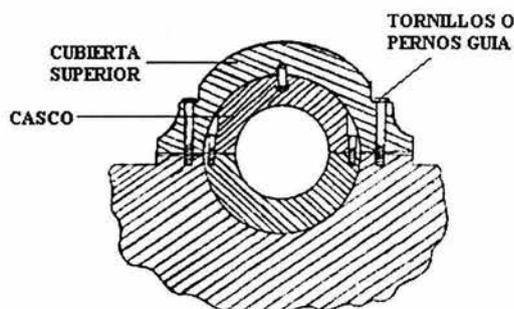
Desmontaje de tornillería en chumaceras.
